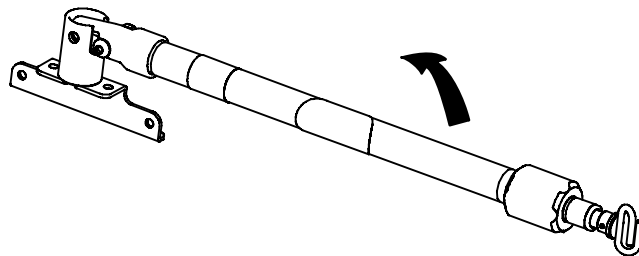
Posizione dell'asta portaflebo a tre sezioni
